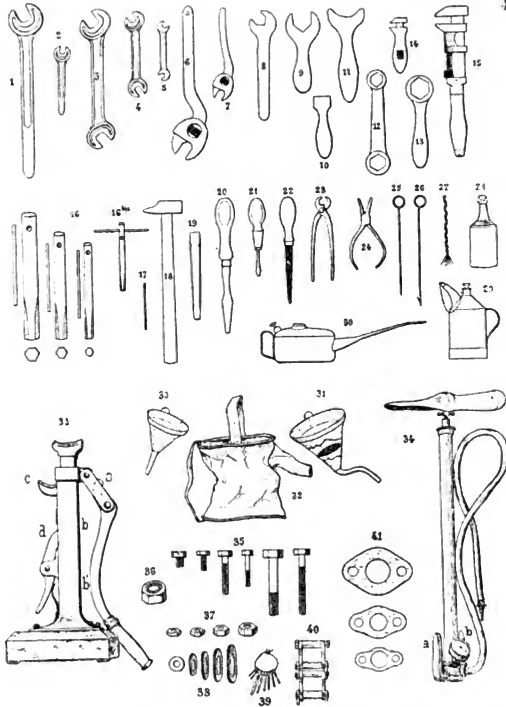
Einige Stücke des zu einem Automobil gehörigen Werkzeuges
